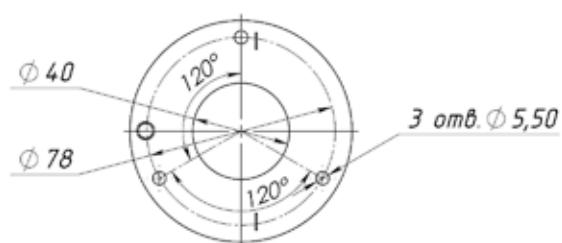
Разъединитель РЕ19-41(43)-72250-00 УХЛЗ на два направления с боковой смещенной рукояткой
